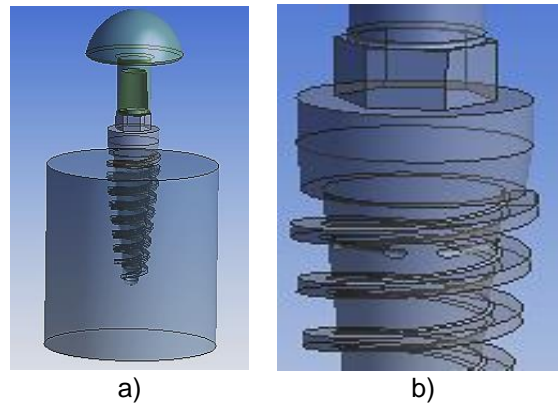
a) Ensamblaje con miembro hemisférico y soporte cilíndrico.
